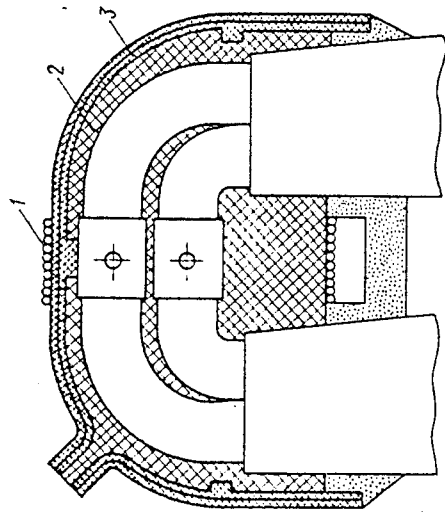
Изолировка и крепление головки обмотки с терморезистивной изоляцией: 1 — шнуровой бандаж; 2 — замазка; 3 — изоляционные коробочки
